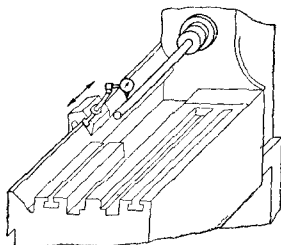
Проверка соосности передней и задней бабок у токарно-винторезного станка.
